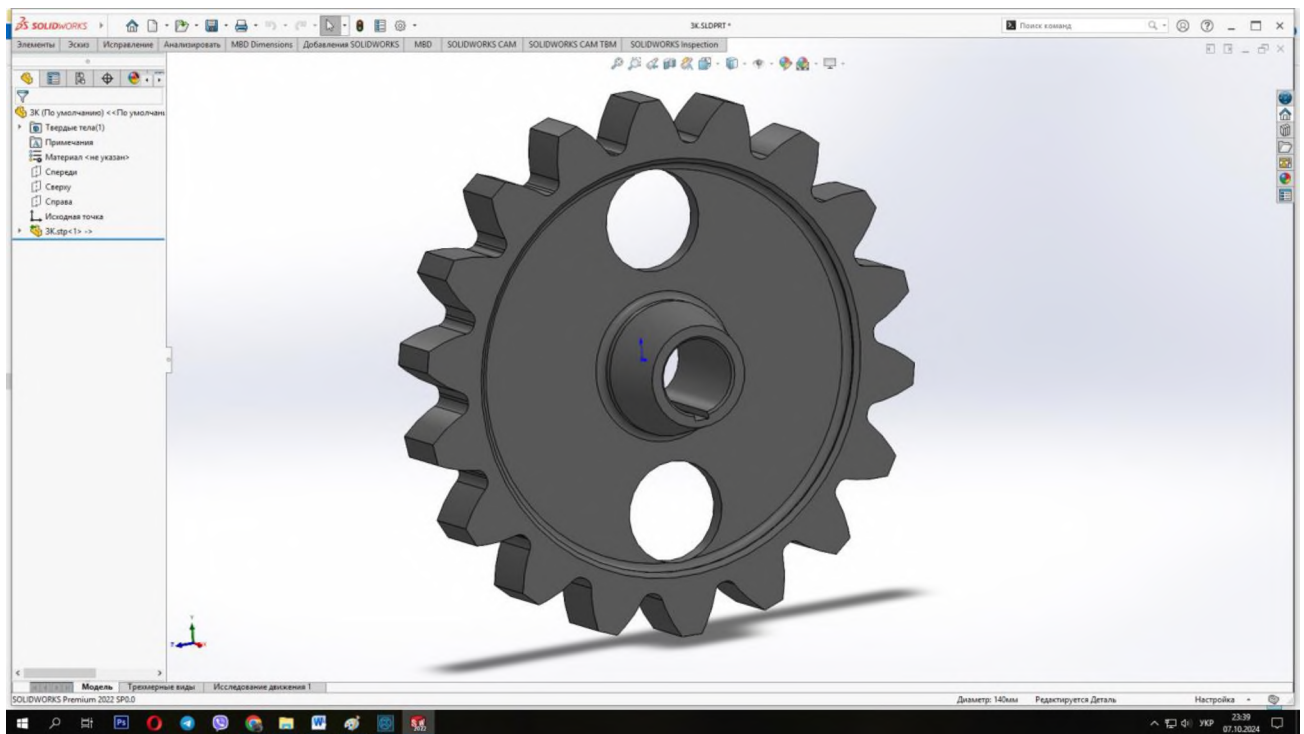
3D-модель зубчастого колеса привода рухомого конвеєра
